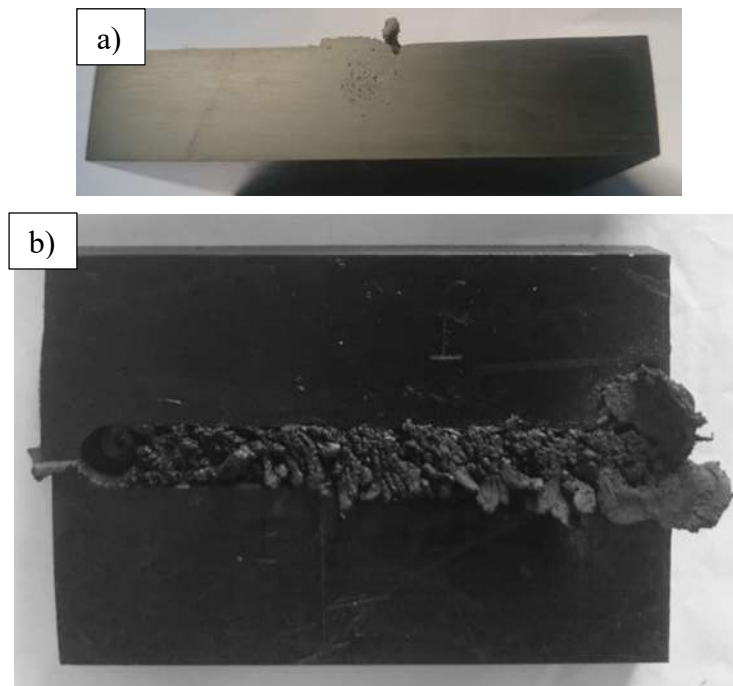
a) Corte transversal FSW de ABS (porosidad) y b) Soldadura ABS (unión 9).
